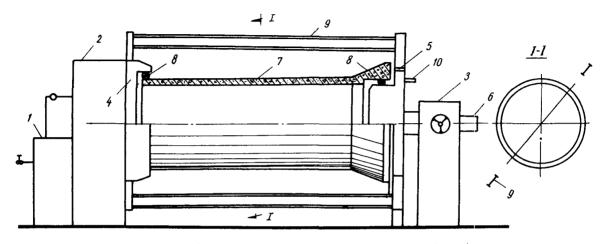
Схема машины для гидравлических испытаний труб I — насосная станция; 2 — задняя опора; 3 — передняя опора; 4 — втулочная планшайба; 5 — раструбная планшайба; 6 — подвижной вал планшайбы; 7 — труба; 8 — резиновые уплотняющие кольца; 9 — продольные тяги; IO — отверстия для удаления воздуха.
